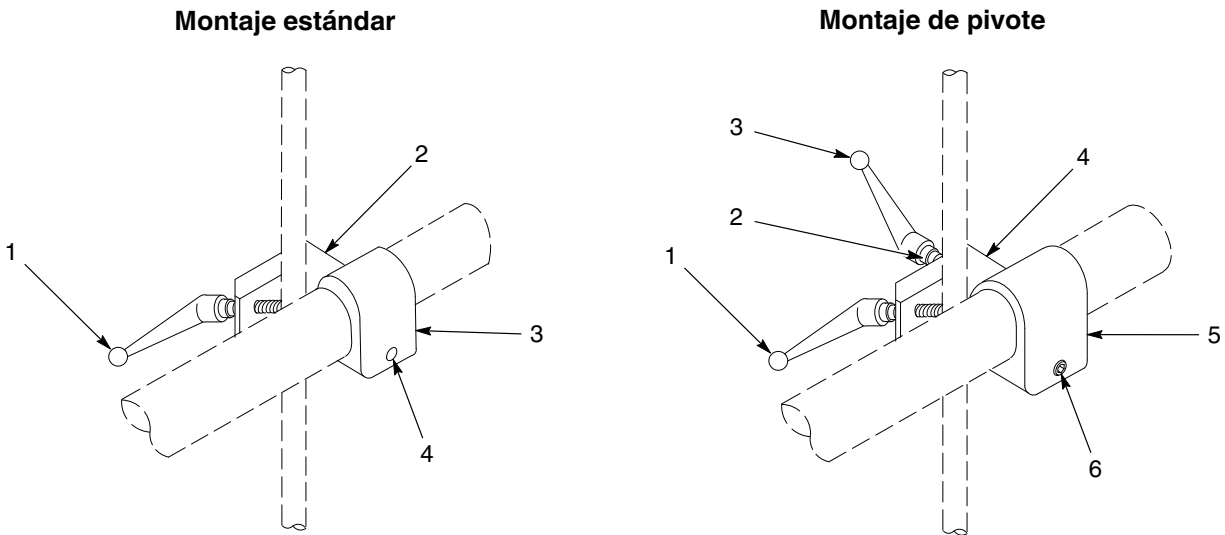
Montajes en barra de pistola para pistolas de montaje en tubo
